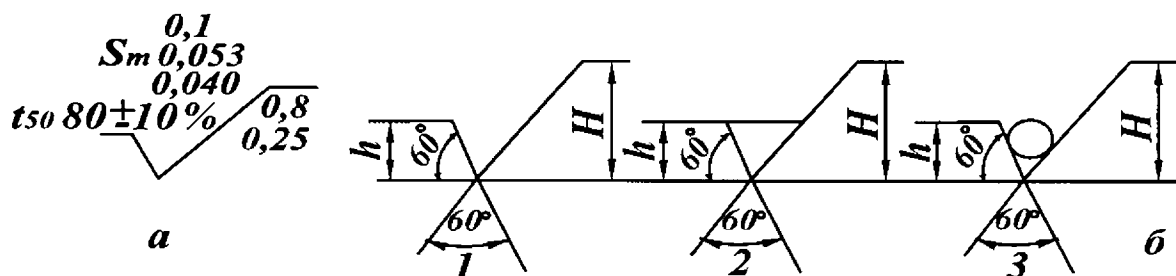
Полная запись шероховатости поверхности (а) и условные знаки обозначения шероховатости (б) ($H=(1,5-3)h$, h – равна высоте цифр размерных чисел на чертеже): 1) без указания метода обработки; 2) с указанием метода обработки; 3) черновые поверхности
